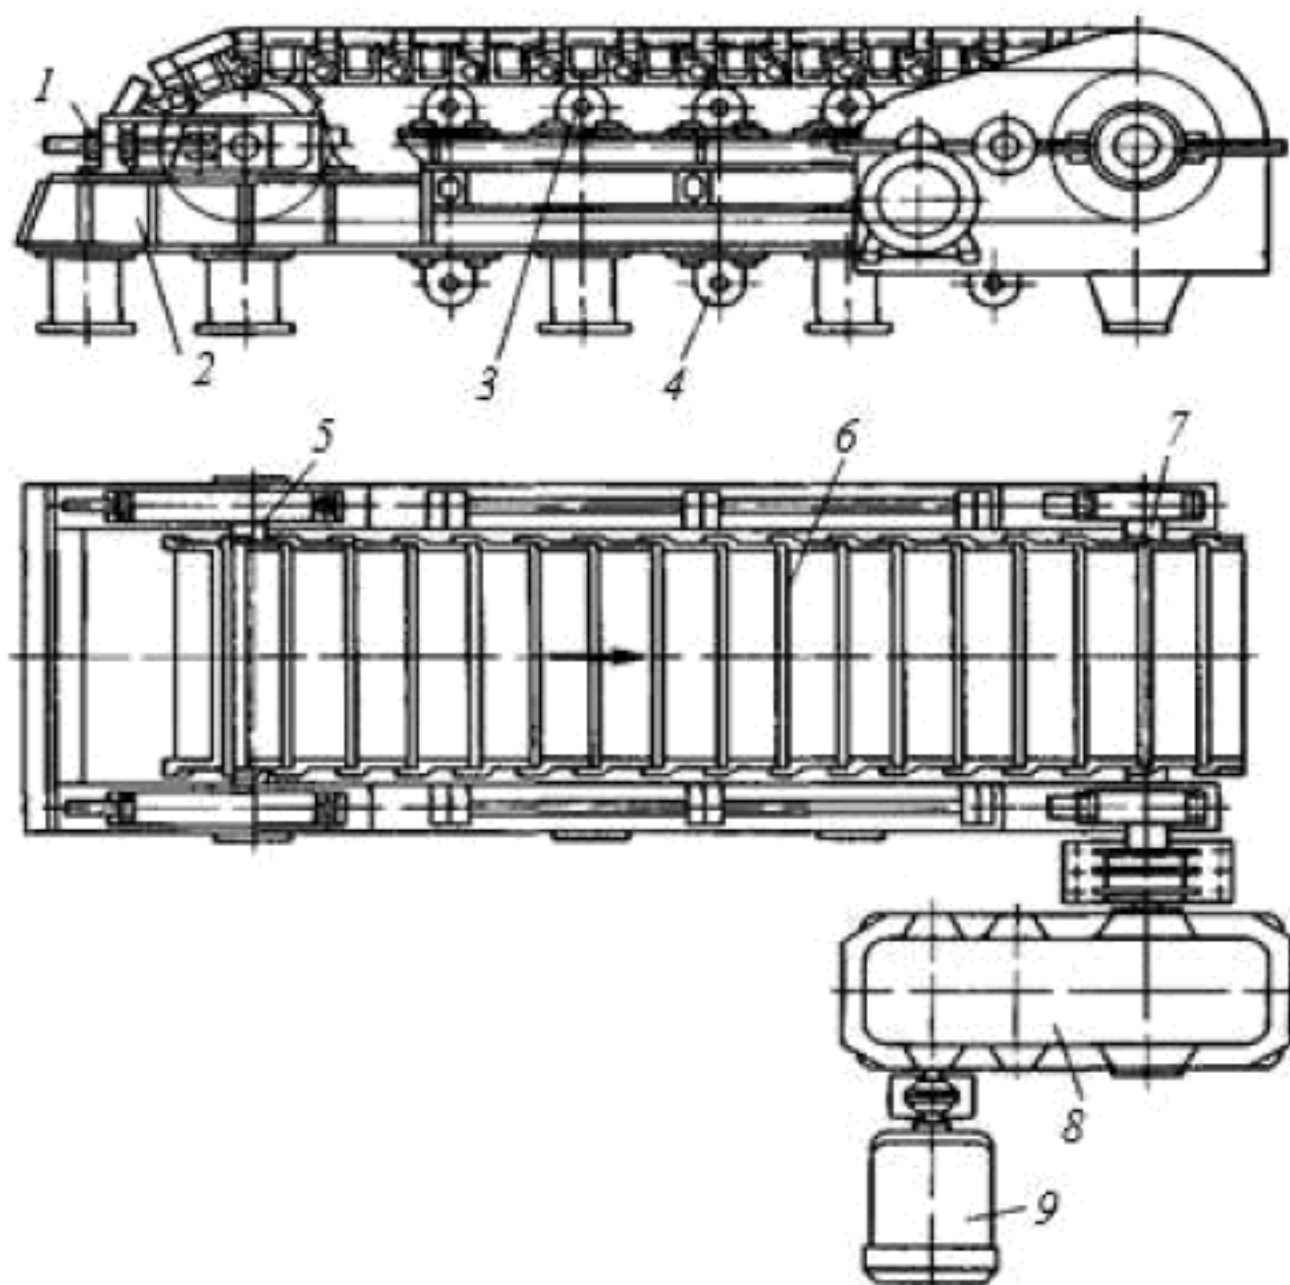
Пластинчастий живильник: 1 – натяжний пристрій; 2 – рама; 3, 4 – верхні і нижні опорні ролики; 5 – ведомий вал із зірочками; 6 – пластинчасте полотно; 7 – ведучий вал із зірочками; 8 – редуктор; 9 – електродвигун [5]
